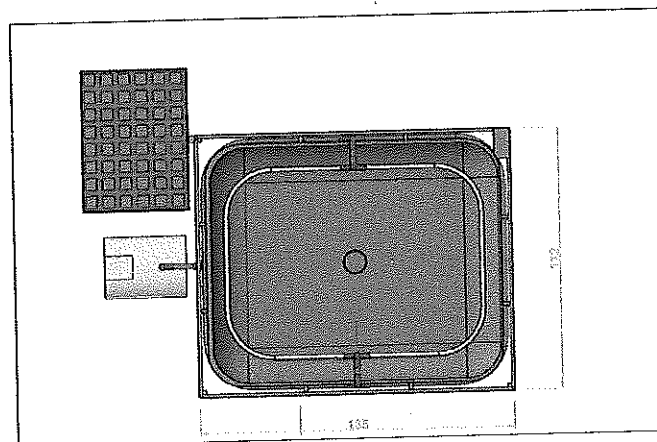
Sistema de riego en nivel 2, para plantas. Vista de planta.
